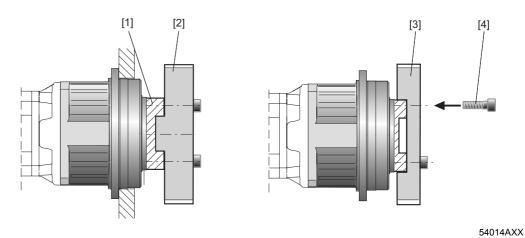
Exemplo de montagem para um bloco de flange PSBF..
